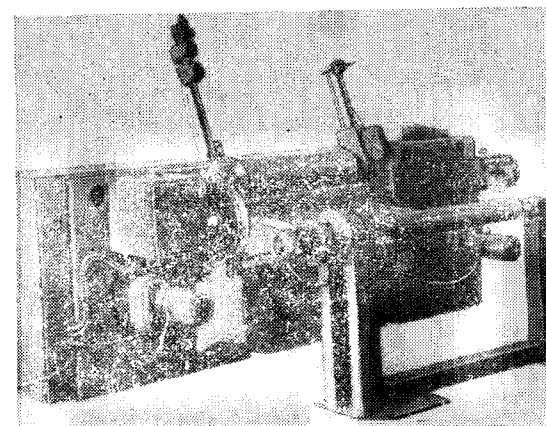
Оборудование для строжки листа с цилиндрической литой заготовки из полиуретана.
